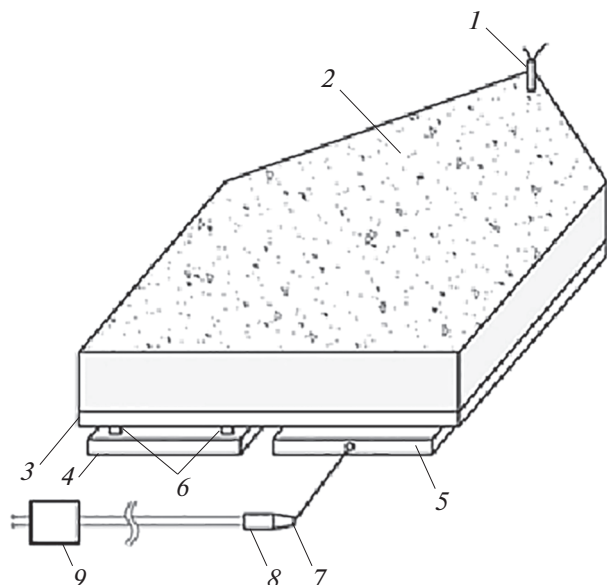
Схема сварки взрывом с воздействием ультразвука: 1 – электродетонатор; 2 – заряд ВВ; 3 – металлическая пластина; 4 – неподвижная пластина; 5 – неподвижная пластина с подводом ультразвуковых колебаний; 6 – опорные элементы; 7 – волновод; 8 – пьезокерамический преобразователь; 9 – ультразвуковой генератор.
